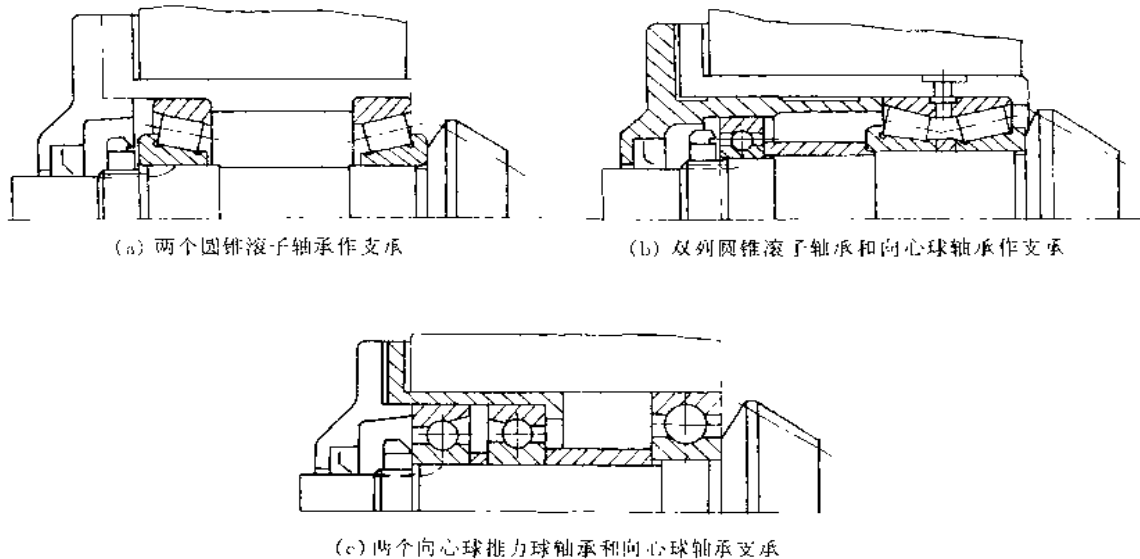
小圆锥齿轮轴上轴承支承结构
